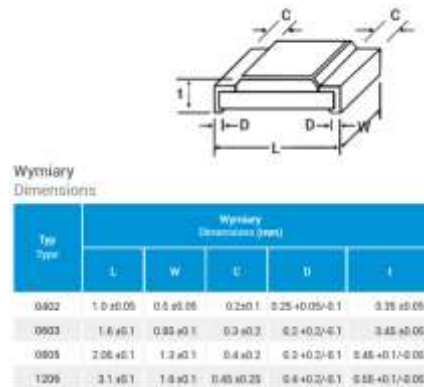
Габаритні розміри SMD-конденсаторів MLCC-SMD/SMT у корпусі 1206
